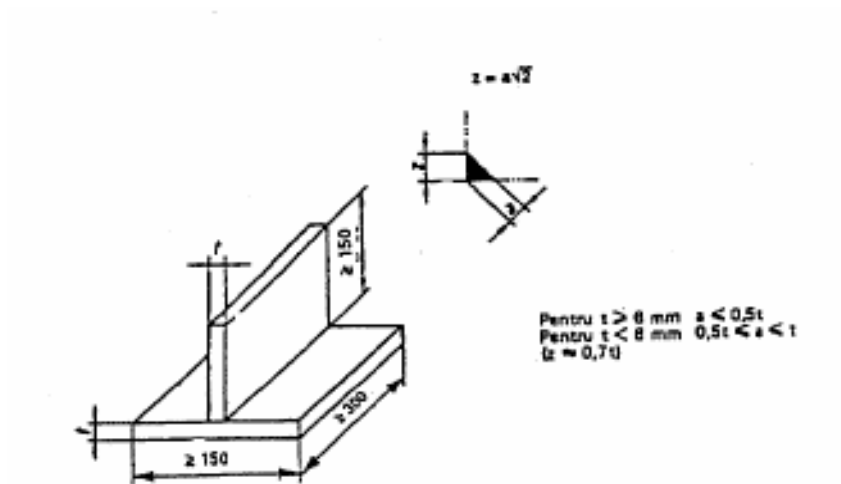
Dimensiunile probei pentru sudura în colț la tablă
